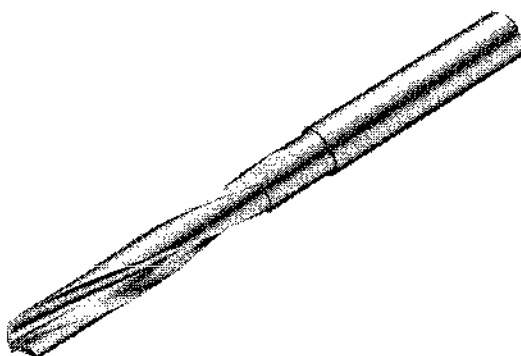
сверло 393 – 393.1-0492-021A1-XM
